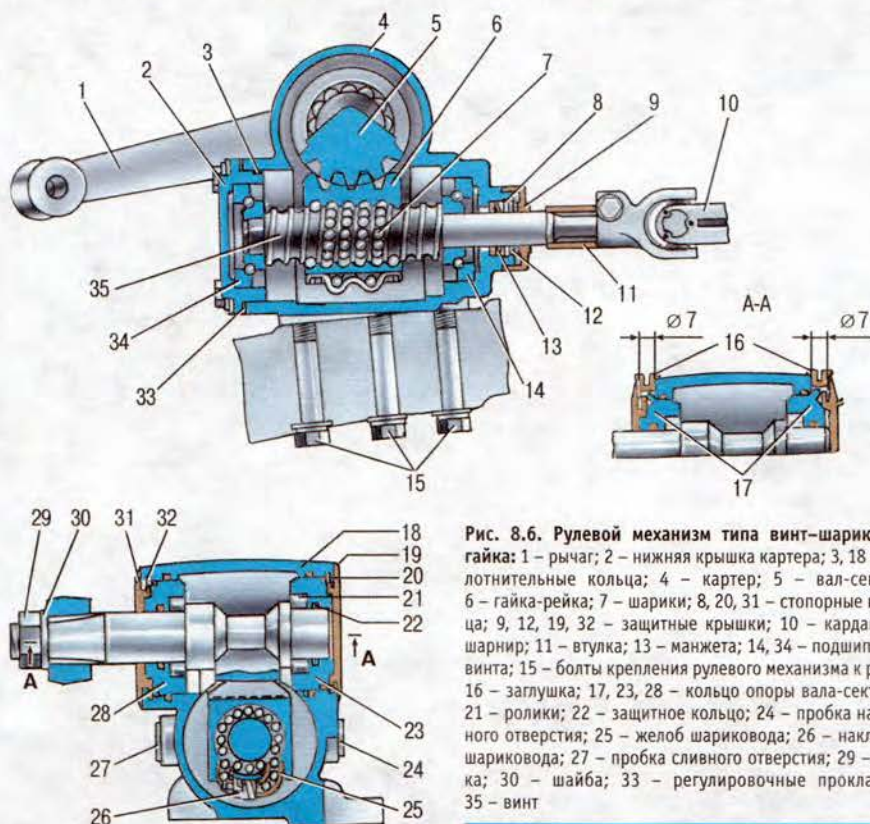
Рулевой механизм типа винт-шариковая гайка: 1 – рычаг; 2 – нижняя крышка картера; 3, 18 – уплотнительные кольца; 4 – картер; 5 – вал-сектор; 6 – гайка-рейка; 7 – шарики; 8, 20, 31 – стопорные кольца; 9, 12, 19, 32 – защитные крышки; 10 – карданный шарнир; 11 – втулка; 13 – манжета; 14, 34 – подшипники винта; 15 – болты крепления рулевого механизма к раме; 16 – заглушка; 17, 23, 28 – кольцо опоры вала-сектора; 21 – ролики; 22 – защитное кольцо; 24 – пробка наливного отверстия; 25 – желоб шариковода; 26 – накладка шариковода; 27 – пробка сливного отверстия; 29 – гайка; 30 – шайба; 33 – регулировочные прокладки; 35 – винт
